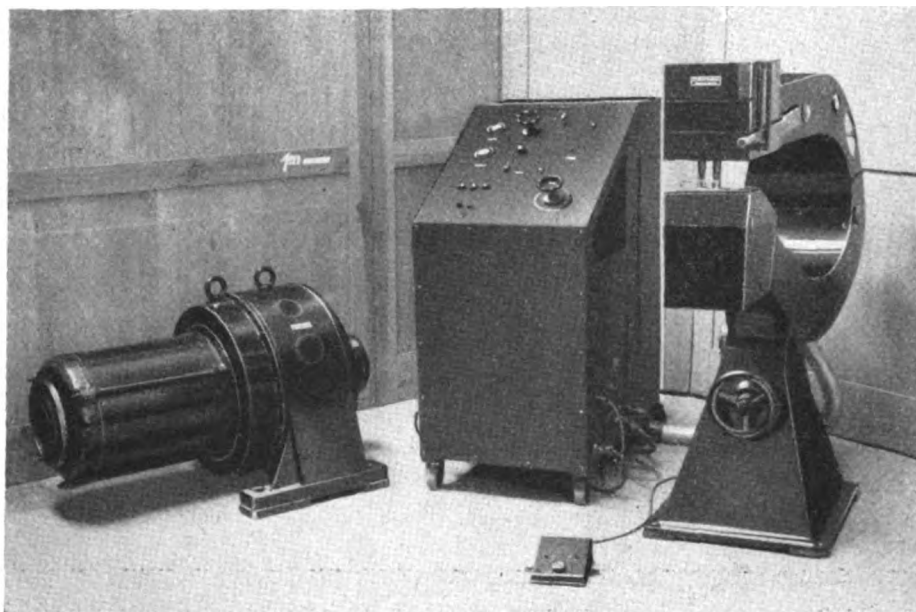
Doppelpunktschweißmaschine für Leichtmetalle.
